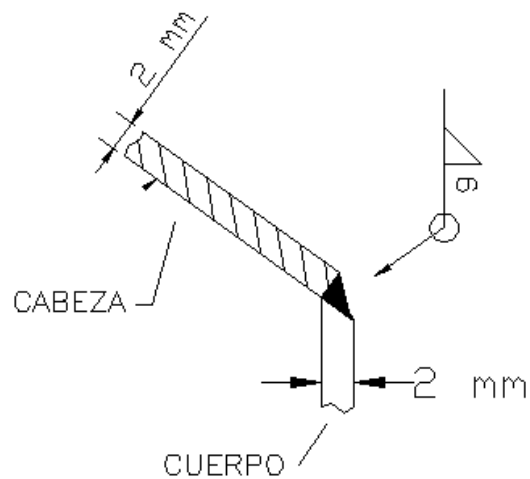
Detalle de la Unión de Soldadura del Conjunto.
